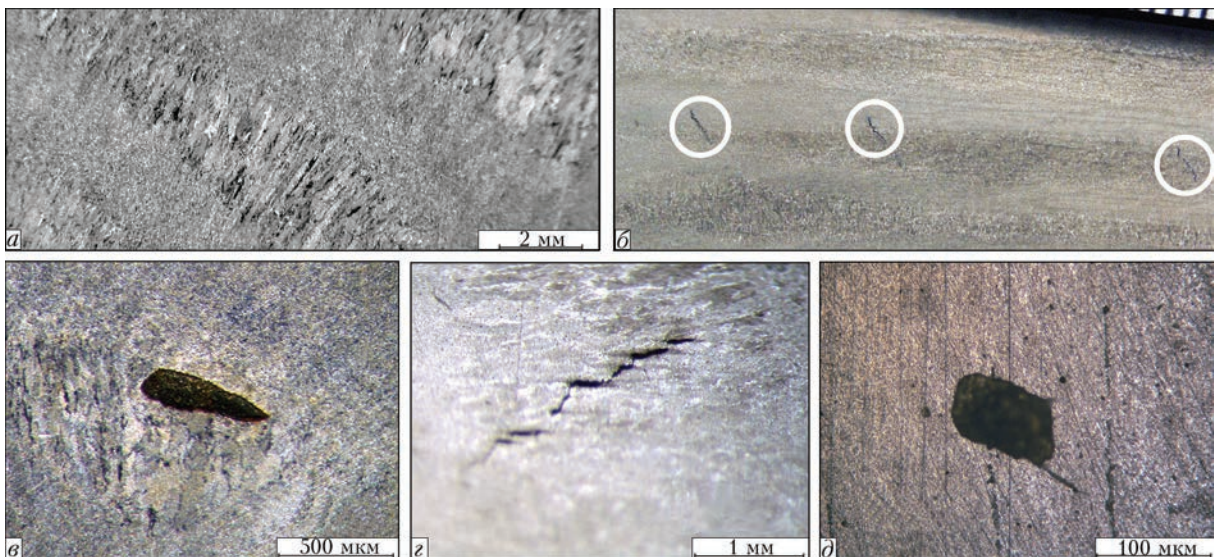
Структура металла сварного шва и выявленные дефекты: а – слоистая структура металла шва; б – макроструктура с трещинами (выделены кругами); в – пора; г – трещина; д – неметаллическое включение
